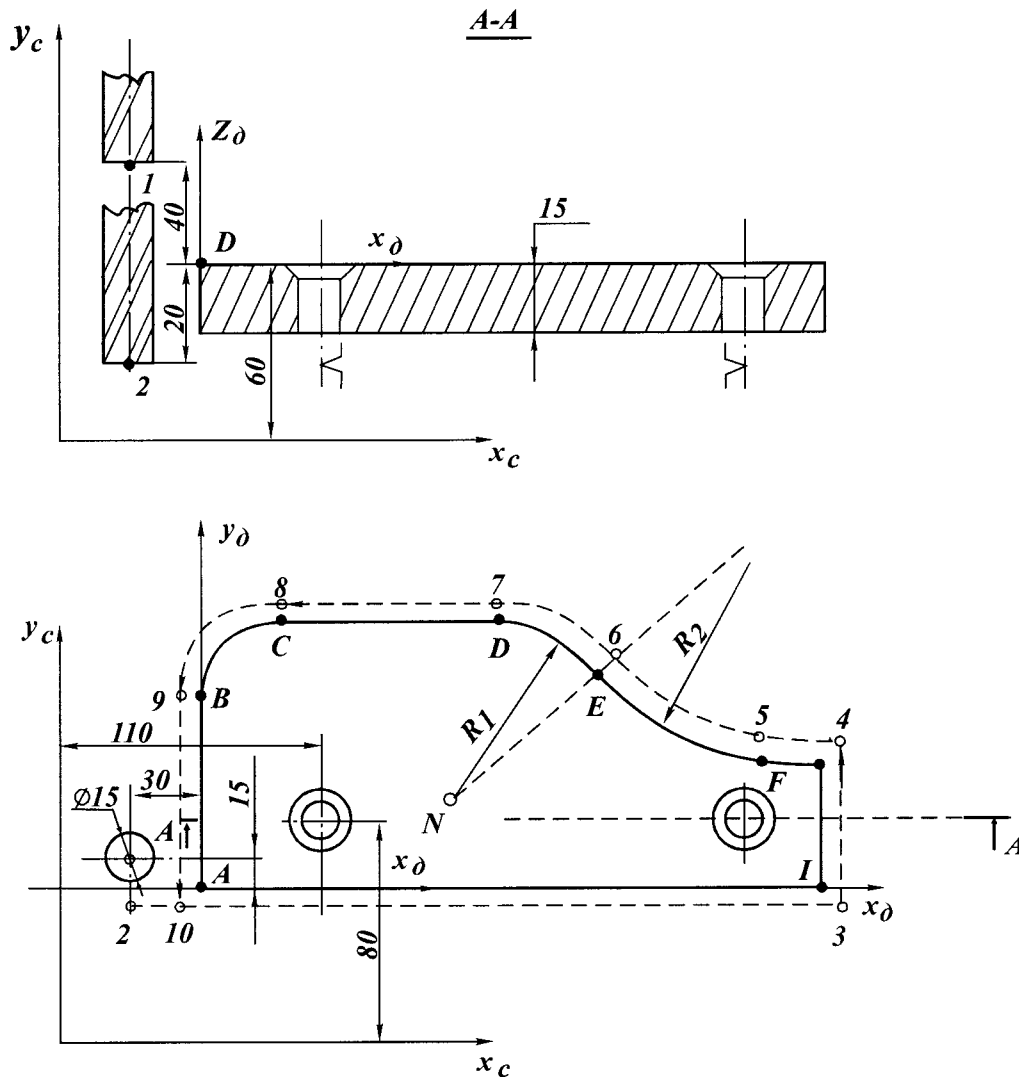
Операційний ескіз фрезерування контуру пластини.
